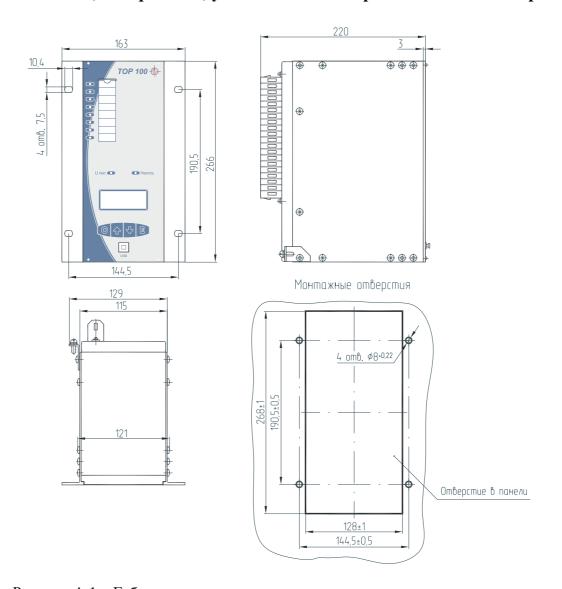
Габаритные и установочные размеры для утопленного монтажа
